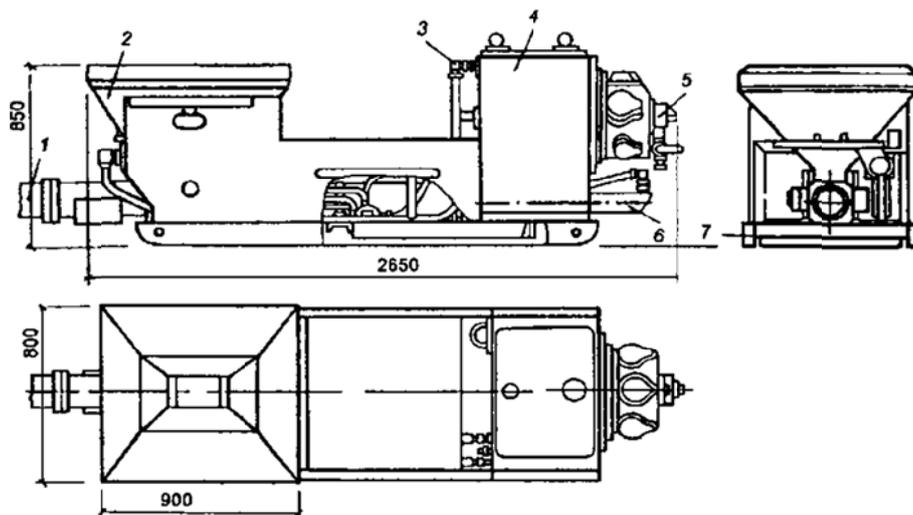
Бетононасос СБ-161: 1 – бетоновод; 2 – бункер; 3 – гидросистема; 4 – гидропривод; 5 – кран; 6 – рабочий цилиндр; 7 – рама
